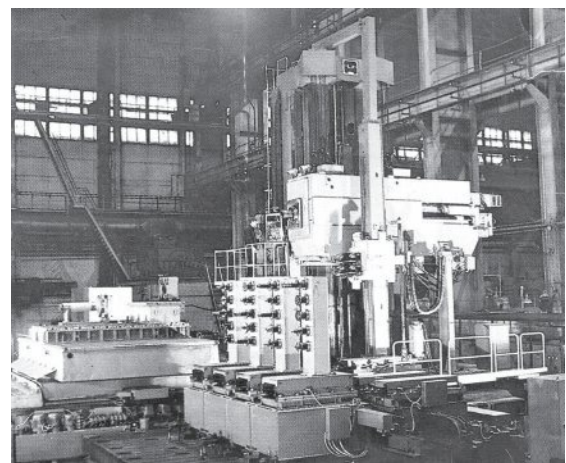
Тяжелый многоцелевой станок сверлильно-фрезерно-расточной группы с поворотным подвижным столом для обработки корпусных деталей массой до 200 т
